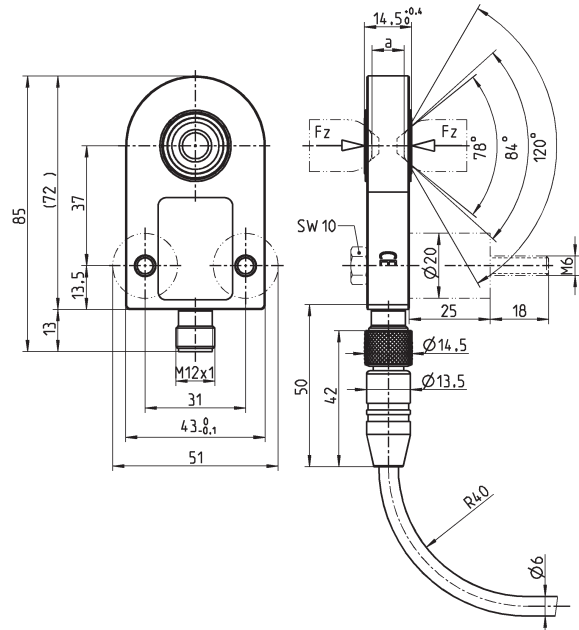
Abmessungen Schweisskraft-Prüftransmitter Typ 9833C1.../C2...
